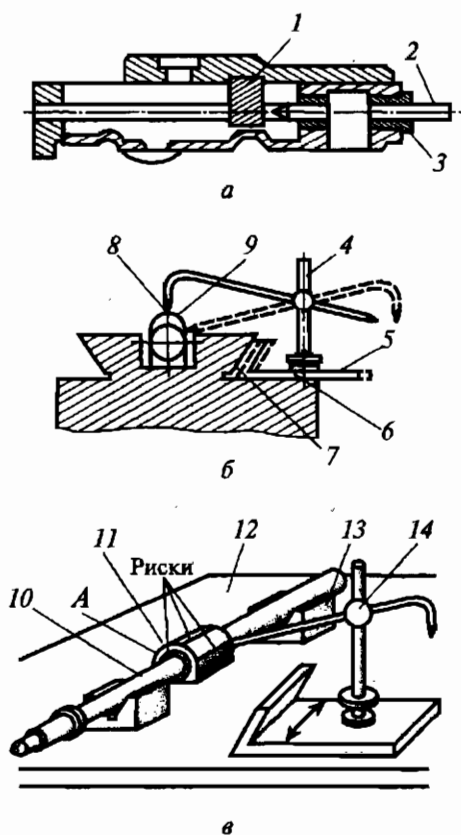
Схема разметки гайки винта: а — накернивание центра на торце гайки; б — нанесение контрольных рисок на поверхность гайки; в — контроль точности расположения оси резьбы гайки; 1 — торец гайки; 2 — кернер; 3 — каретка суппорта; 4 и 14 — рейсмасы; 5 — подставка; 6 и 7 — базовые поверхности; 8 и 9 — верхняя и боковая риски; 10 — винт; 11 — гайка; 12 — контрольная плита; 13 — призмы
